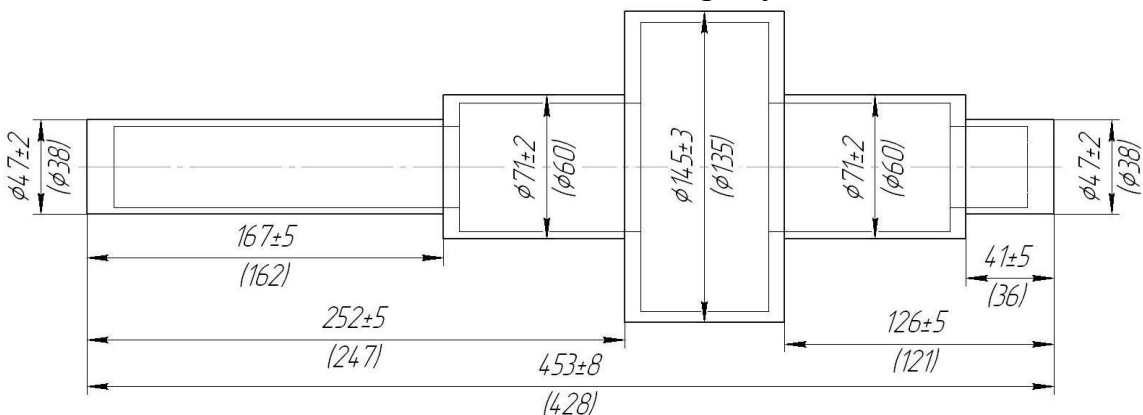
Ескіз заготовки з основними припусками та додатковими припусками
